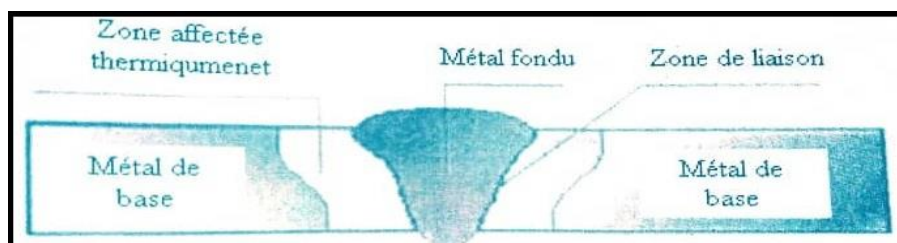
Les différentes zones d'un assemblage soudé [37]
